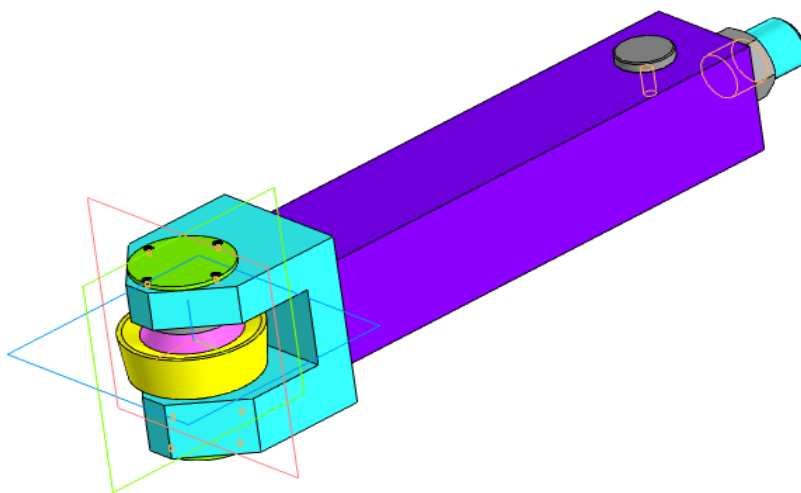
Ротационный безвершинный поворотный токарный резец со стружколомом
